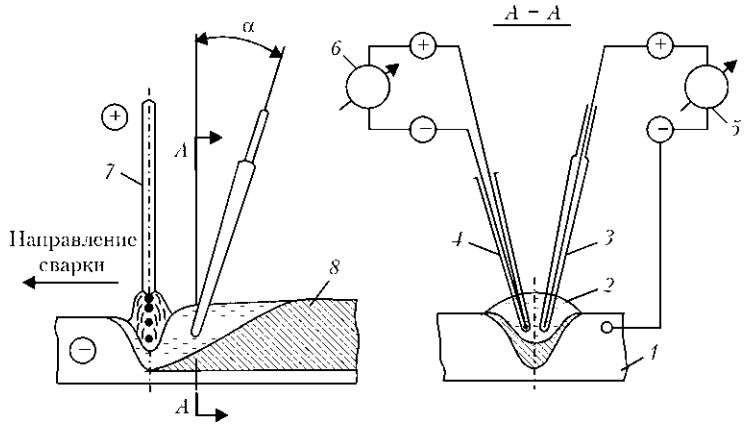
Принципиальная схема экспрессного контроля активности кислорода в металле сварочной ванны: 1 — свариваемый металл; 2 — сварочная ванна; 3 — датчик окисленности; 4 — термопара; 5, 6 — измерительные приборы; 7 — сварочный электрод; 8 — сварной шов; α — угол наклона датчика и термопары, равный 15...20°
